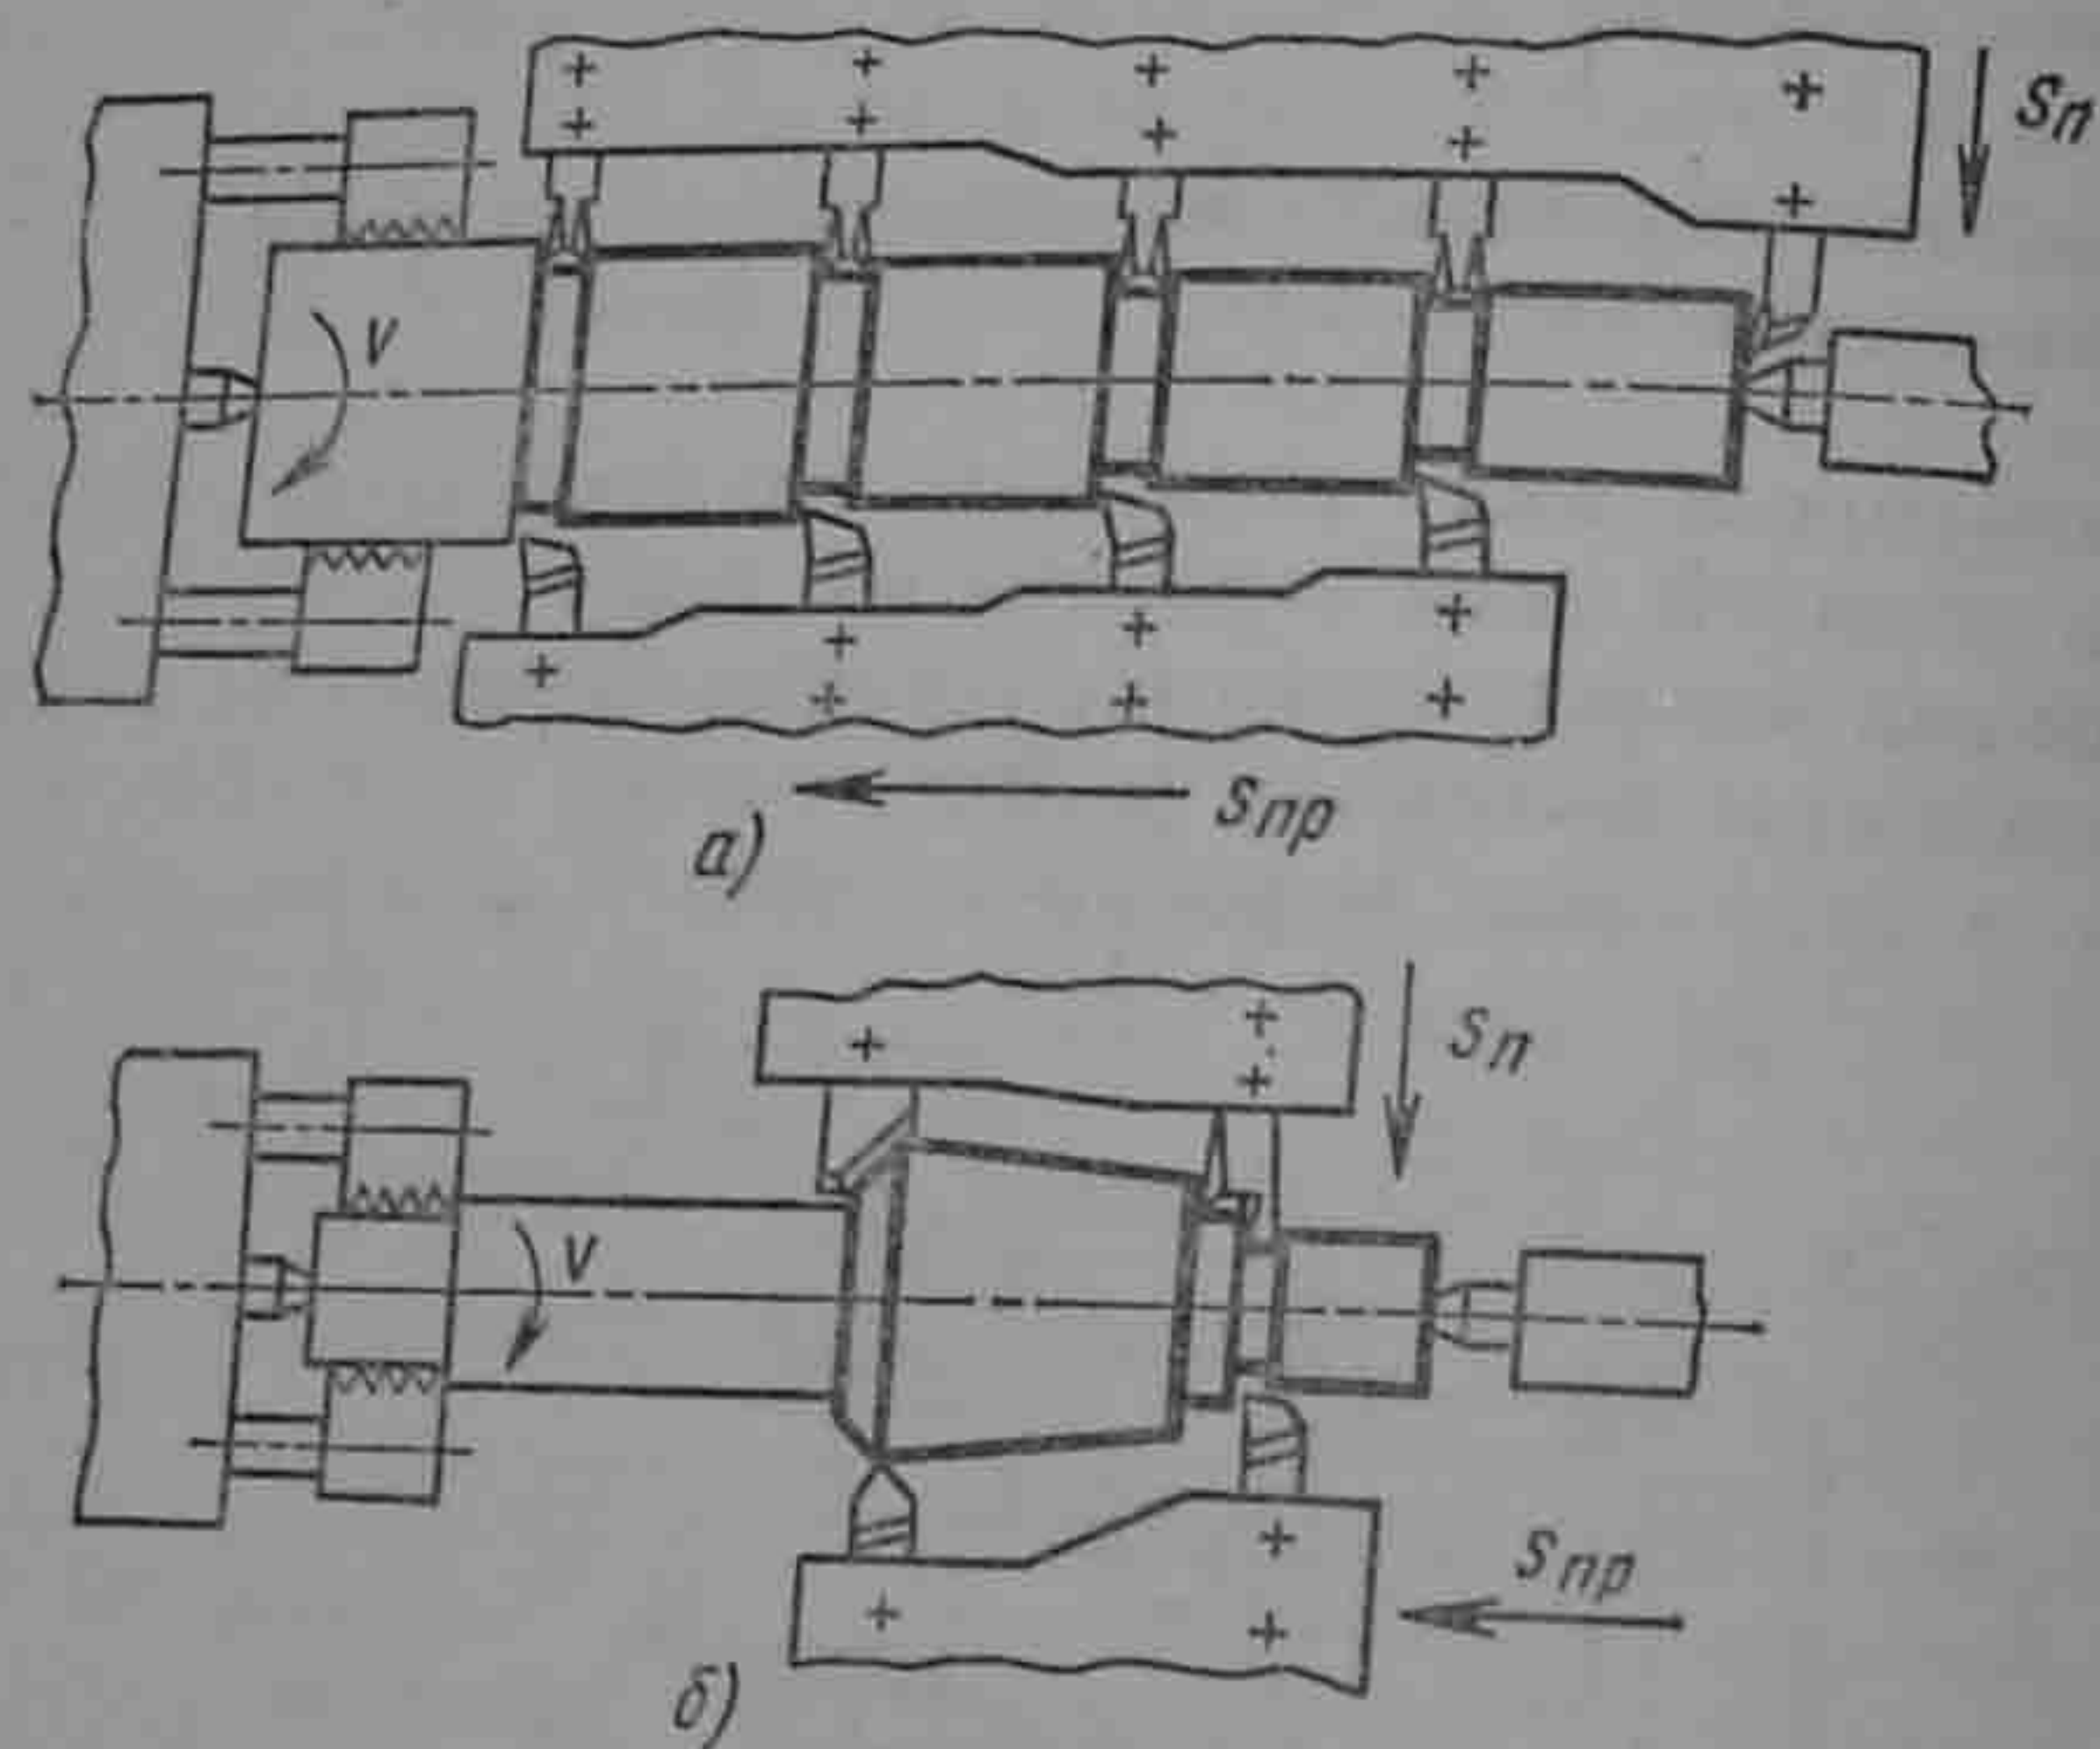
Схемы обработки заготовок на токарном много-резцовом полуавтомате
